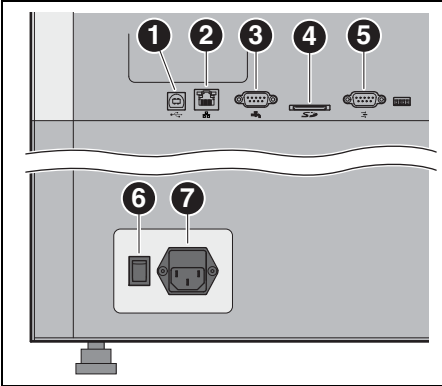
Interfaces sur la face arrière de la fraiseuse
